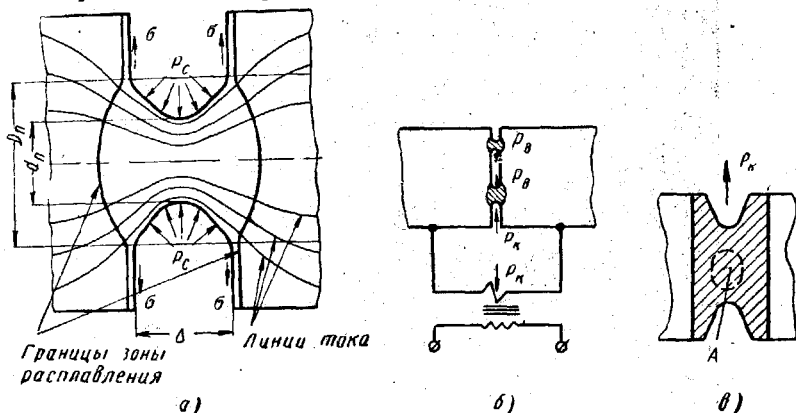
Форма соединения при сварке оплавлением:
